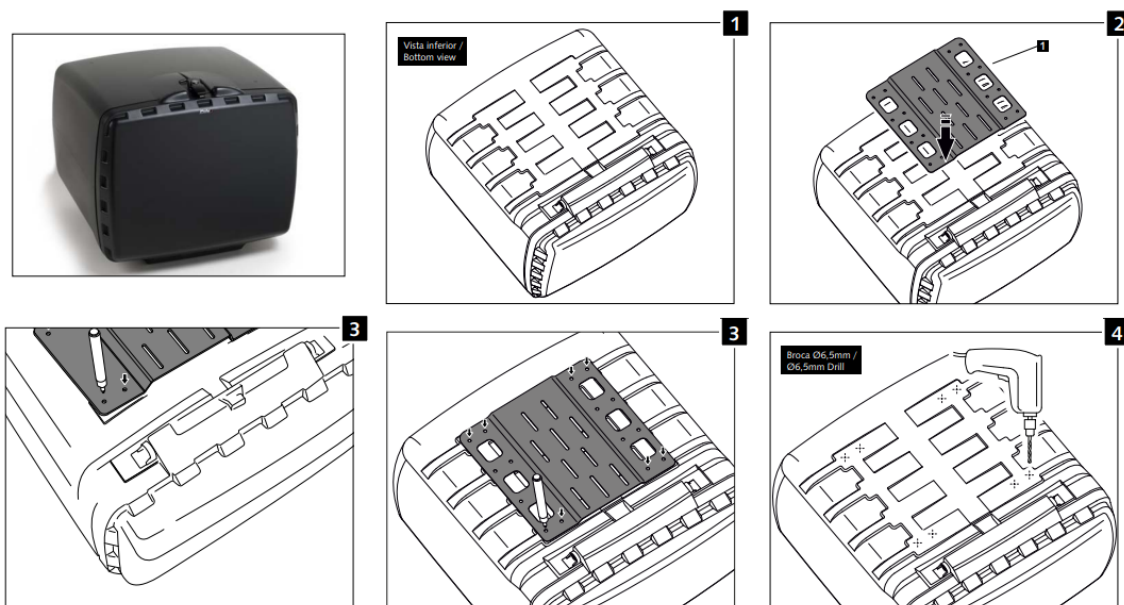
Instrucciones de montaje base metálica. Marca Puig (secuencias 1-4).
